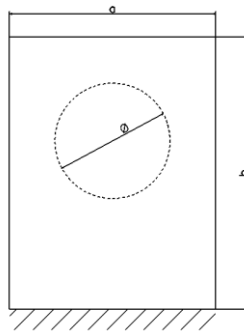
Dimensiones de la placa soporte del filtro polarizador.
